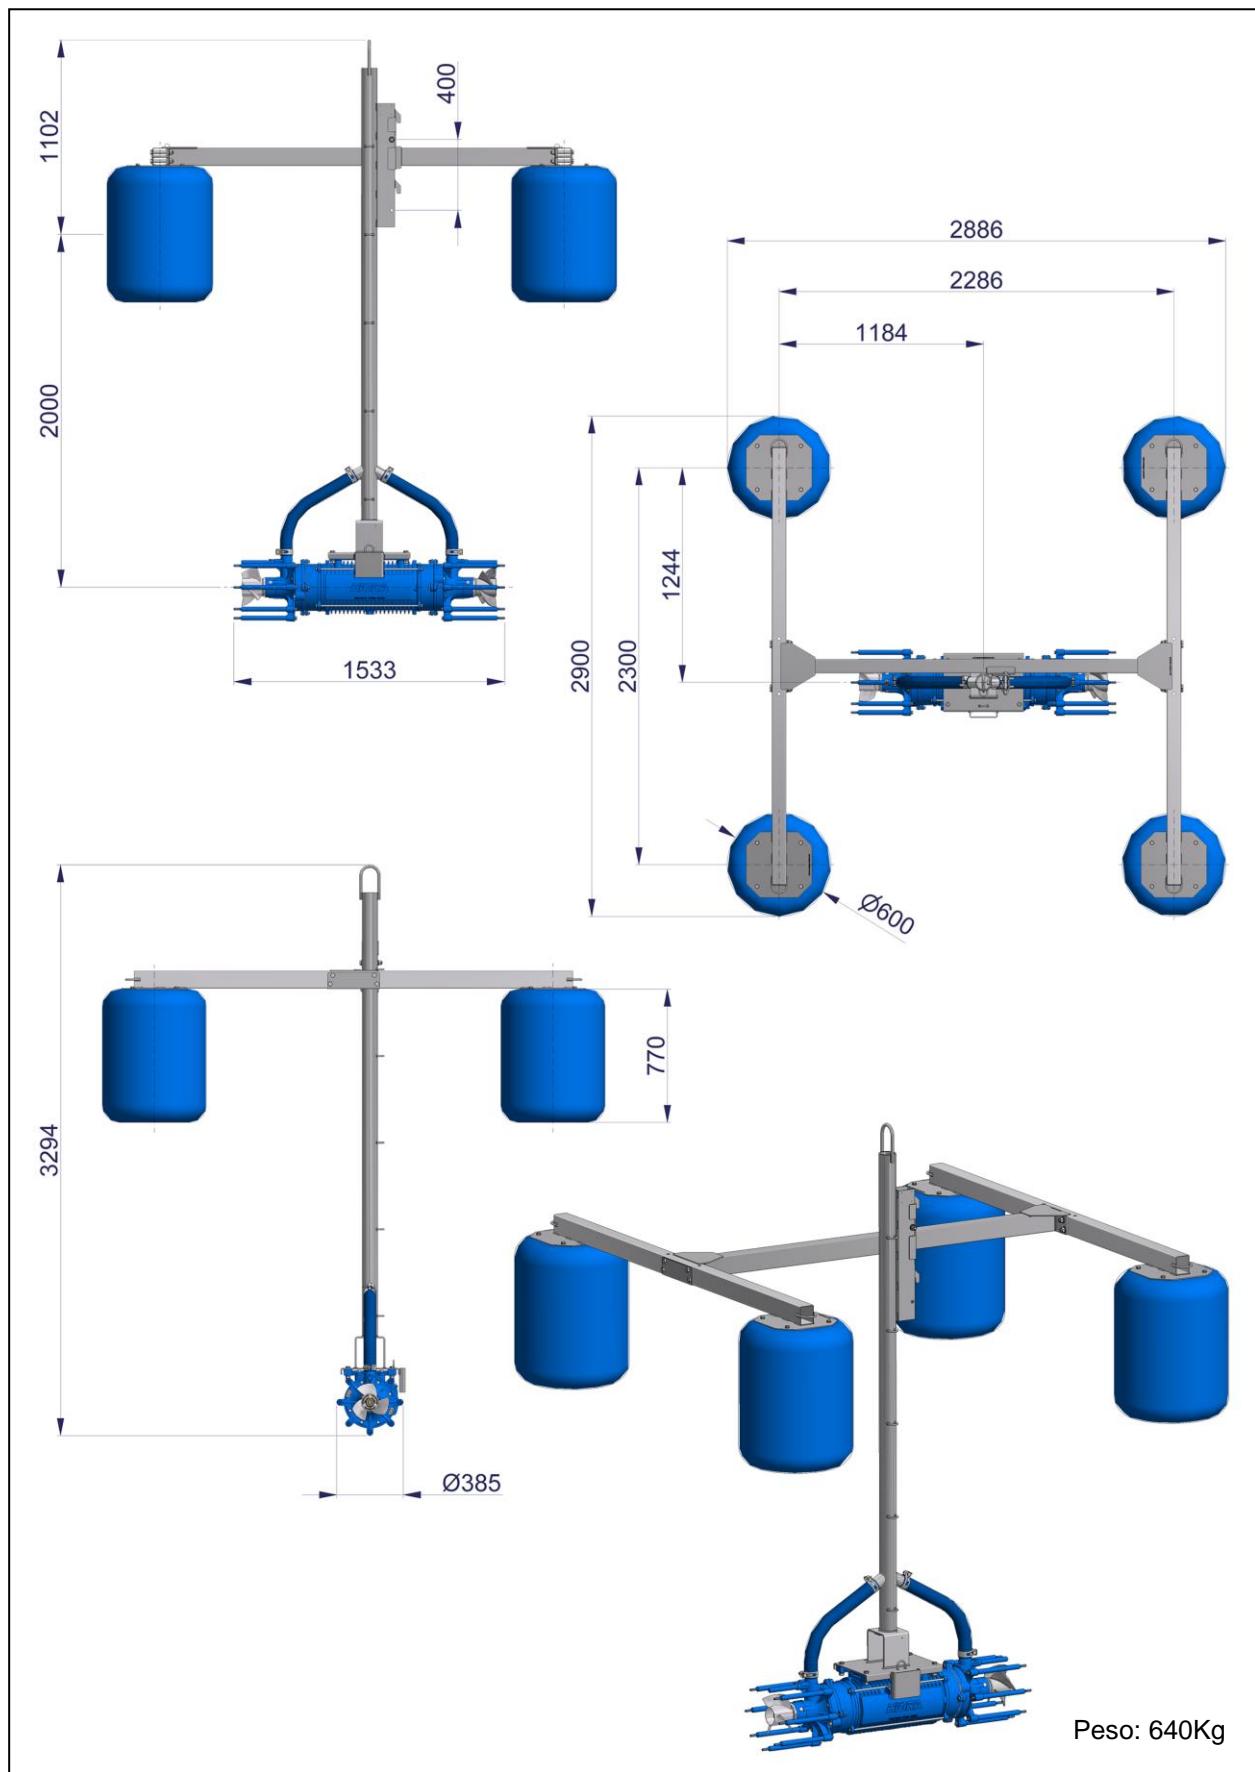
Dimensional TORNADO BITURBO 50,60 e 80CV
